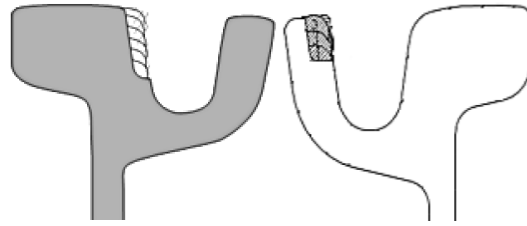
Raupenanordnung der Schweißung (30)
